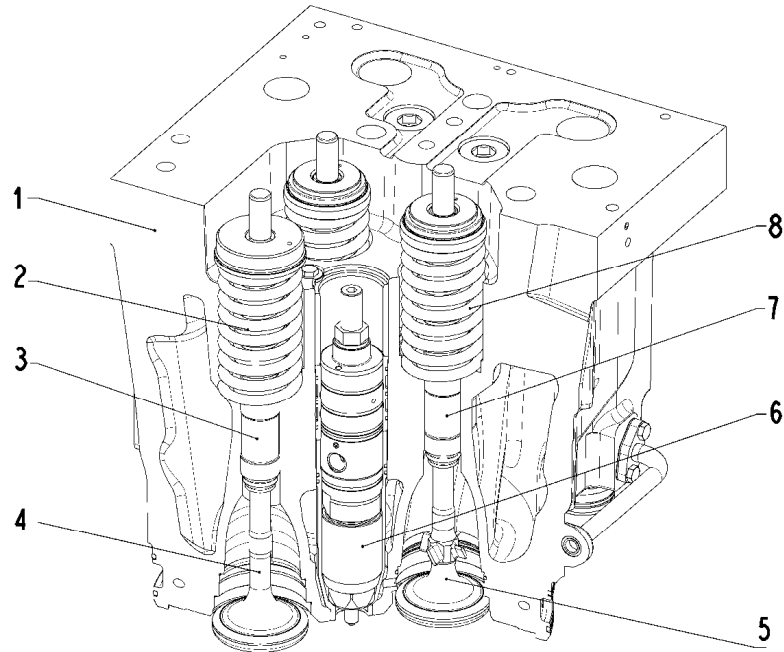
Кришка циліндру з вирізом: 1 – корпус; 2, 8 – пружина клапану; 3, 7 – направляюча втулка клапану; 4 – впускний клапан; 5 – випускний клапан; 6 – форсунка
